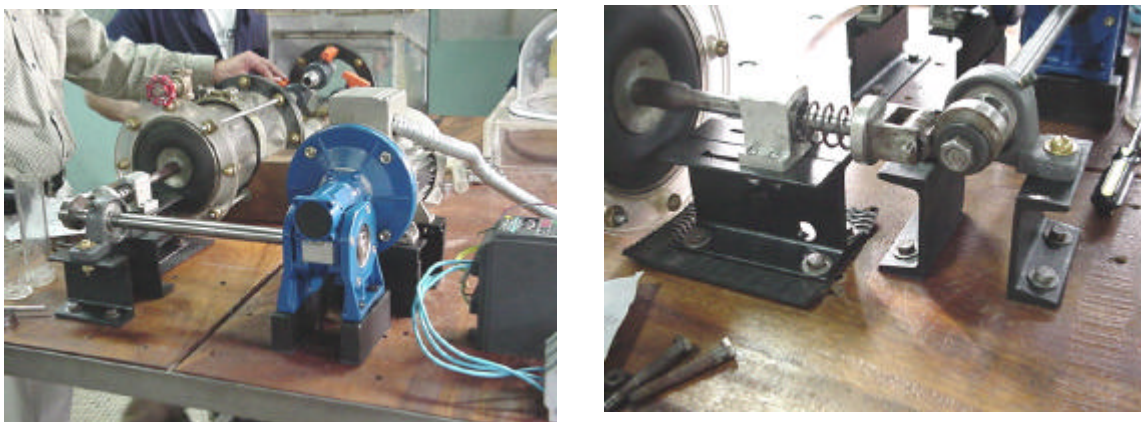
Ensamble de el conjunto leva-seguidor, y conjunto motor-reductor.
